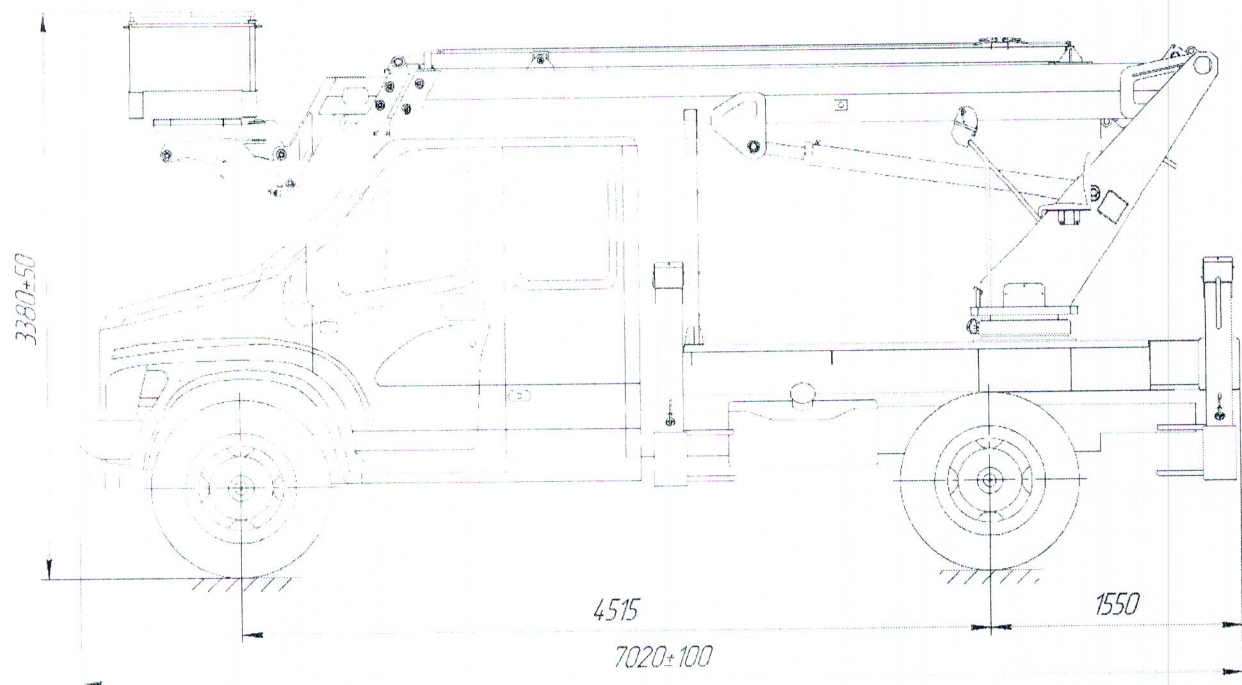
Габаритные размеры подъемника на базе шасси ГАЗ- С42
